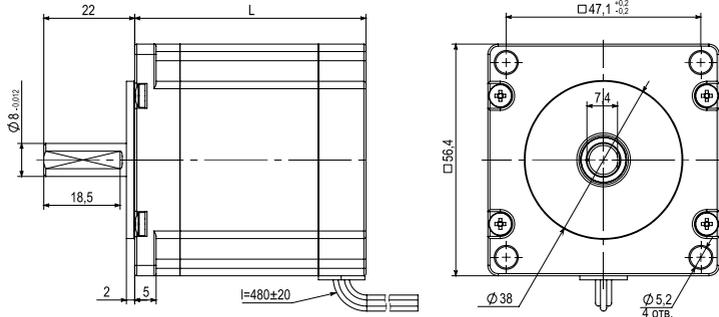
габаритные размеры шаговых двигателей серии SMO-23
